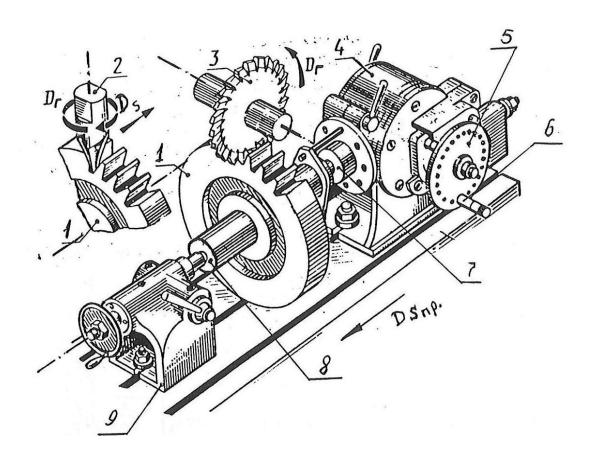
Схема нарезная зубьев методам копирования на фрезерном станке:
